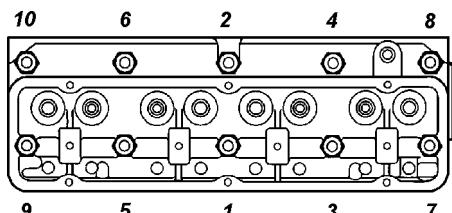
Порядок подтяжки гаек головки блока цилиндров
